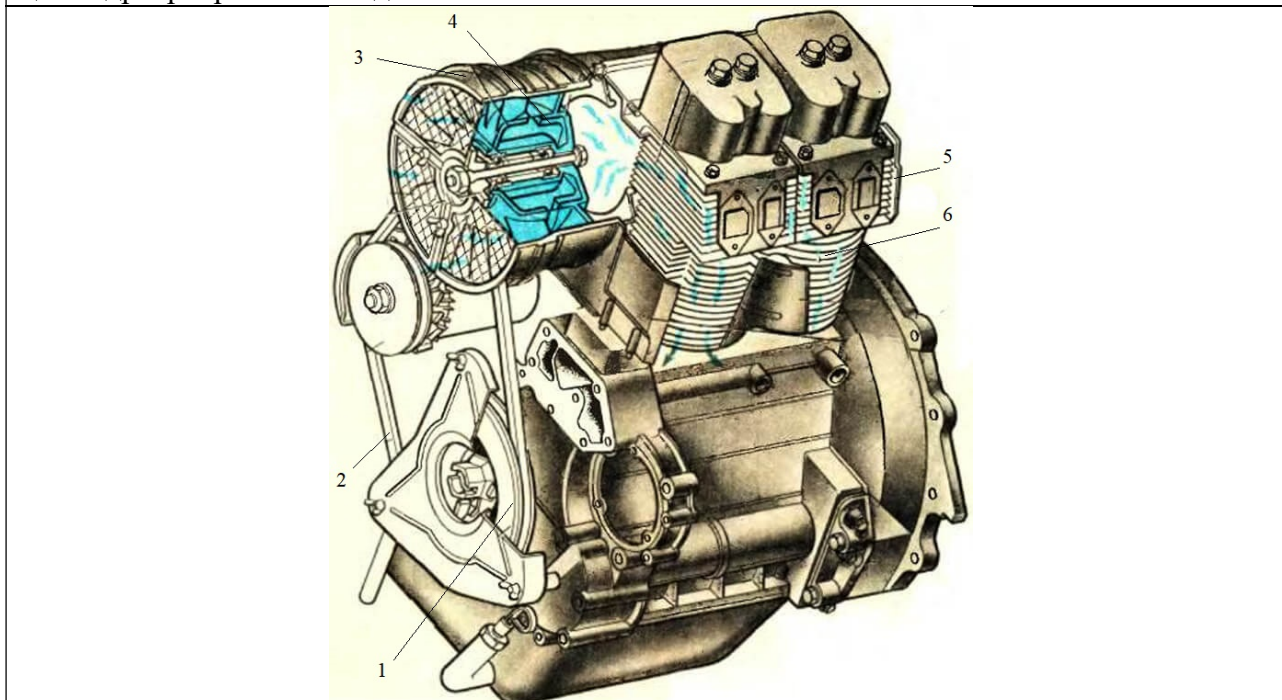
Автомобильный двигатель с принудительной воздушной системой охлаждения: 1 – шкив коленвала; 2 – ремень привода вентилятора; 3 – вентилятор принудительного охлаждения; 4 – направляющее устройство; 5 – головка цилиндра с рёбрами охлаждения; 6 – цилиндр с рёбрами охлаждения
